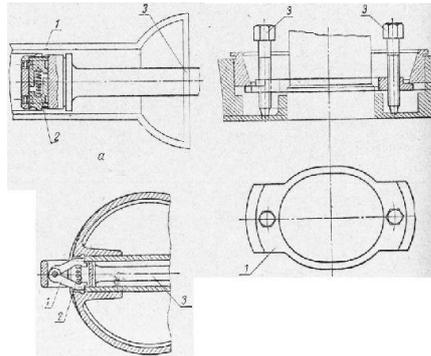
Захваты специального назначения: а к б — для деталей, расположенных глубоко в корпусах; в - для деталей, в середине которых находится длинный вал; 1 — захваты; 2 — пружины; 3 — силовой винт
